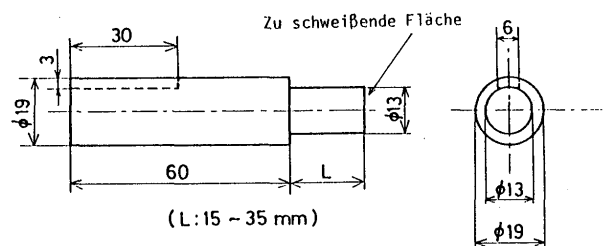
Abmessungen der TPC-Probe für die Messung des Reibungsmoments.
